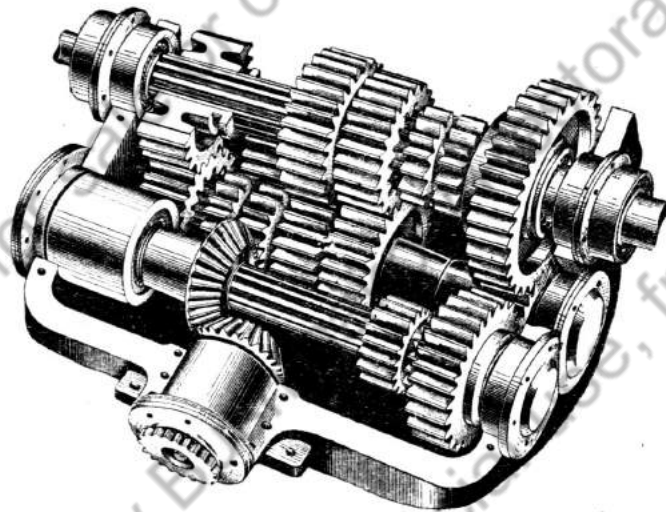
Общий вид коробки перемены передач со снятой верхней крышкой
